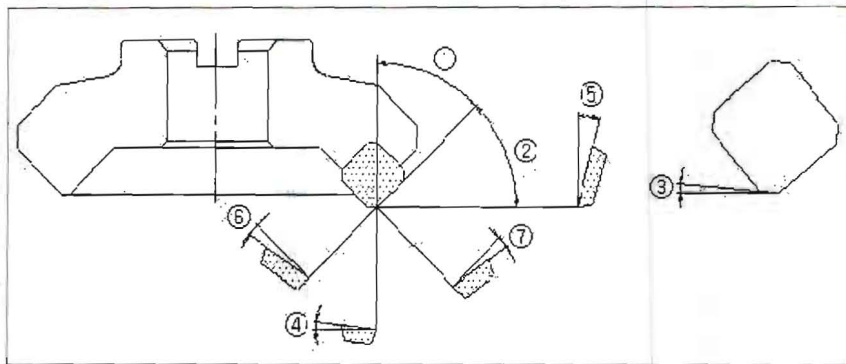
CUTTER BODY 공구각(날 부분의 각)
